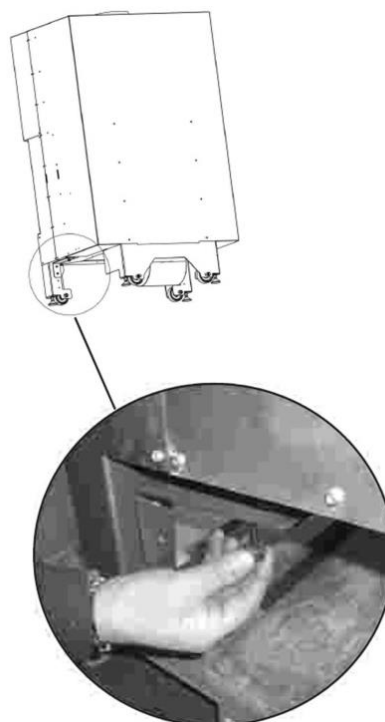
Zugang zum Lösen der Befestigungsschrauben des Gegengewichts
